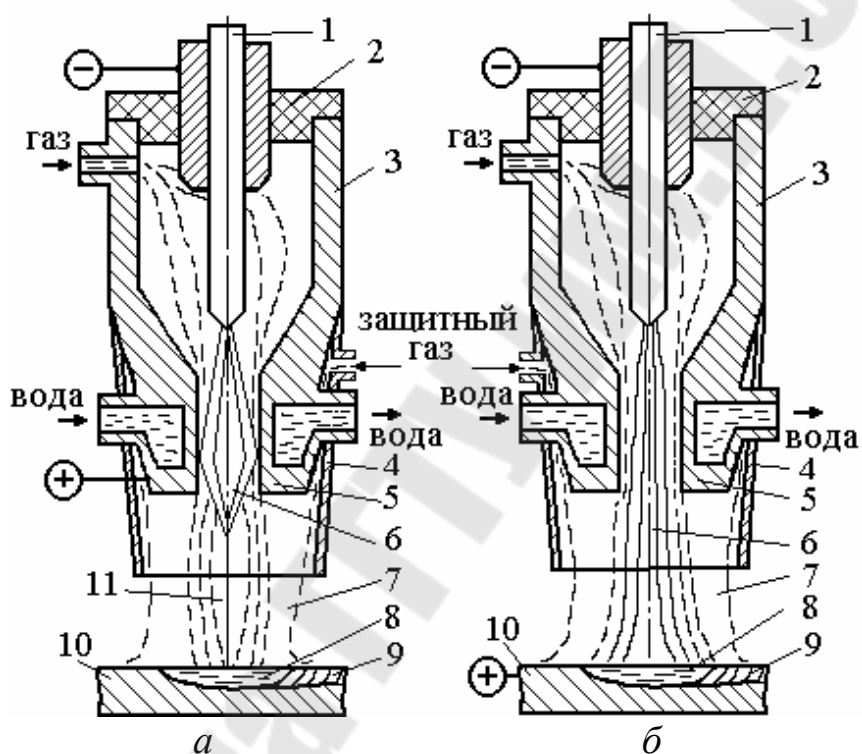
Схема плазменной сварки: а - горелка для генерации плазменной струи, б- горелка для генерации плазменной дуги; 1- неплавящийся (вольфрамовый) электрод, 2- керамическая прокладка, 3- корпус, 4- сопло для защитного газа, 5- сопло горелки, 6- дуга, 7- защитная газовая атмосфера, 8- ванна расплавленного металла, 9- сварной шов, 10- основной металл, 11- плазменная струя
